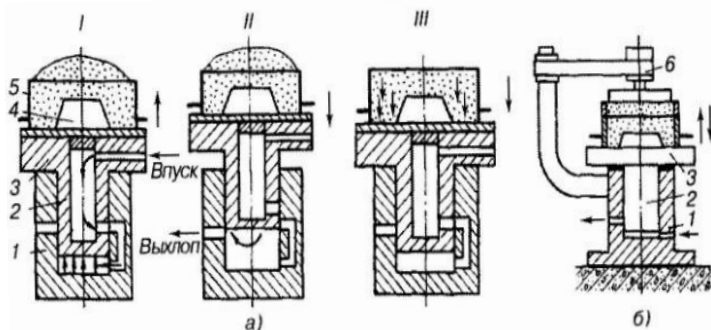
Схема уплотнения формовочной смеси встряхиванием (а) и встряхиванием с подпрессовкой (б); 1 - станина; 2 - поршень; 3 - стол машины; 4 - модель; 5 - опока; 6- прессовое устройство
